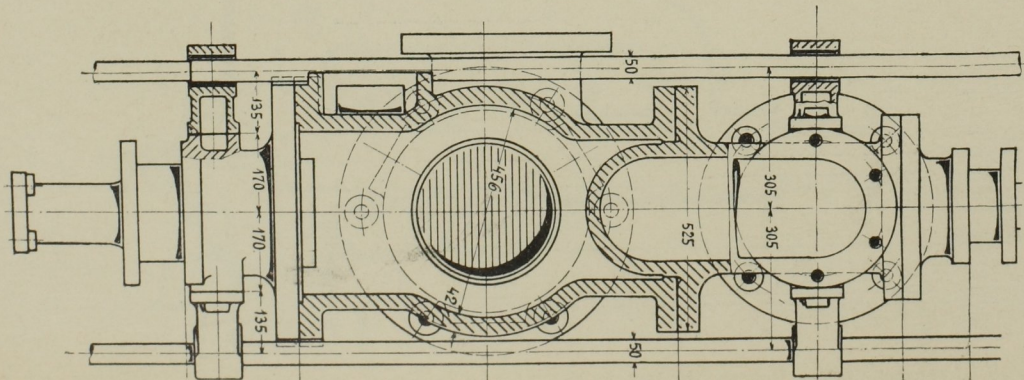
Grundriss der Pumpe. Masst. 1:15.
